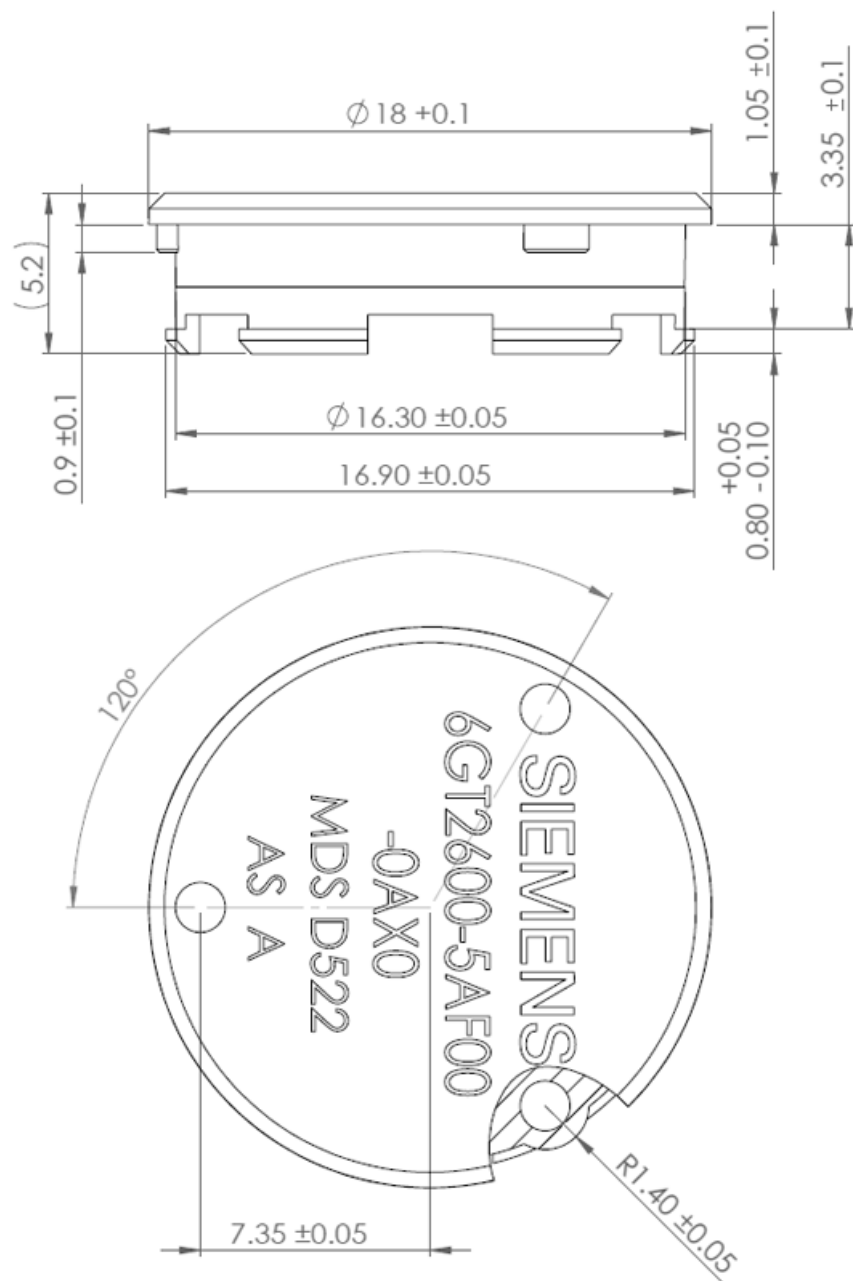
Desenho de dimensões variante especial do MDS D522
